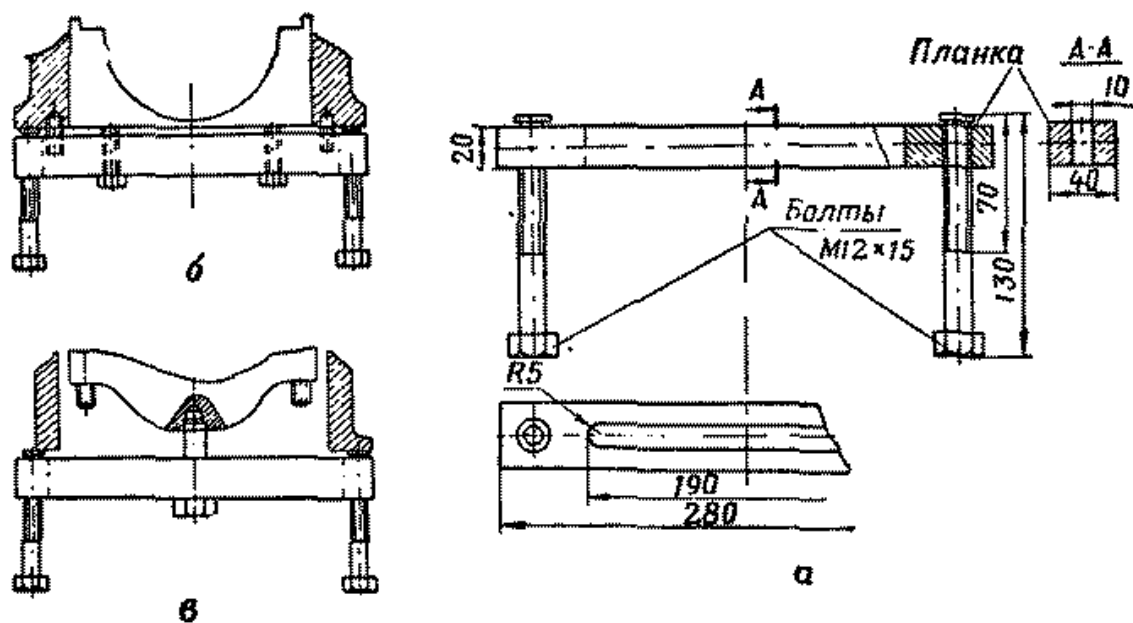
Приспособление для снятия крышек коренных подшипников и дер-
